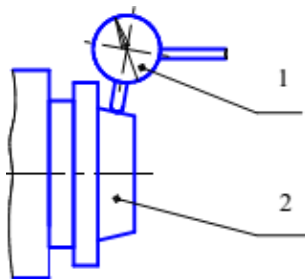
Схема измерения радиального биения центрирующей поверхности шпинделя передней бабки под патрон
